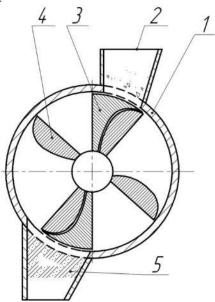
Пресс для отжима протеиносодержащей массы: 1 – корпус; 2 – загрузочная горловина; 3 – лопасть особой формы;
